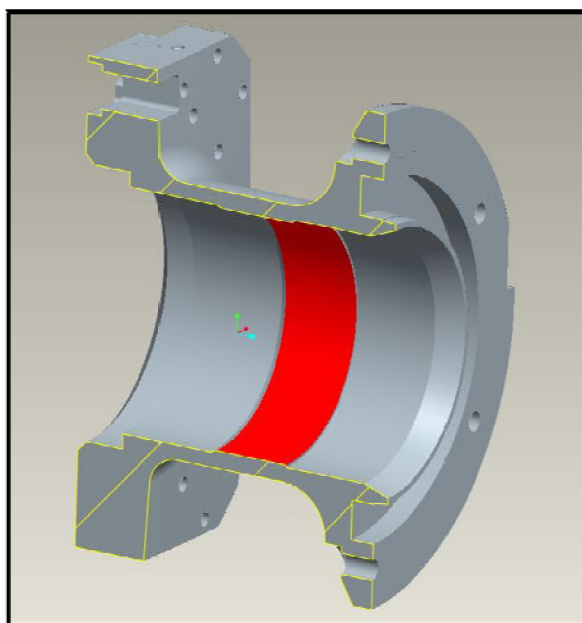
Hlavní konstrukční prvky vyvrtávací U-Hlavy
